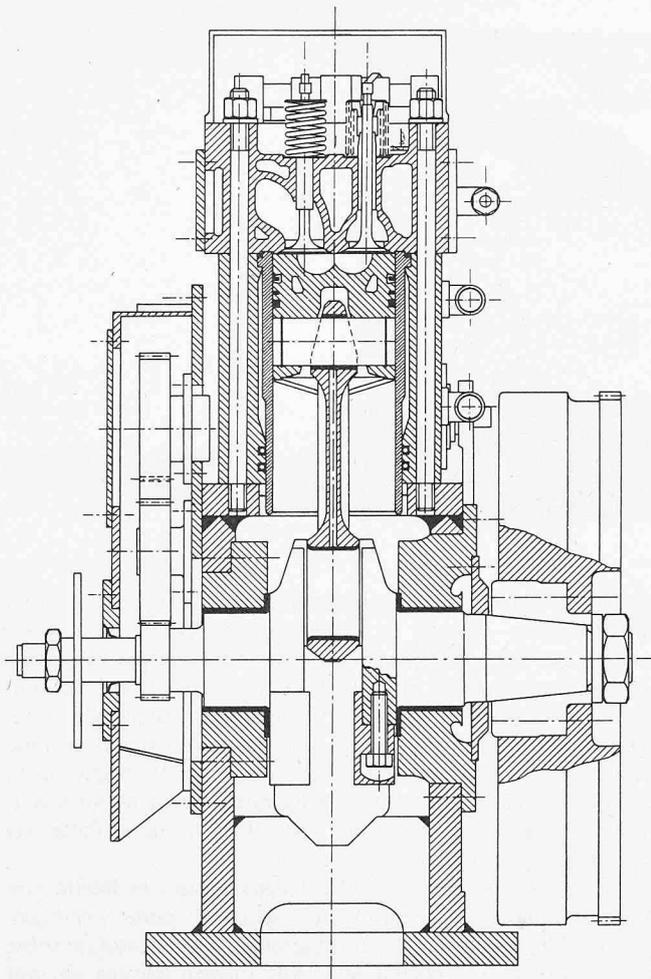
Ansicht des Motors mit Zylinderkopf, Kraftstoffpumpe und Einspritzdüse
